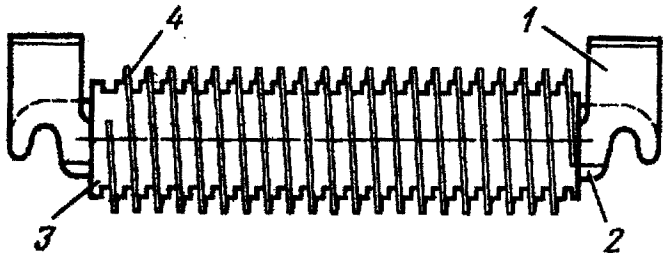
Внешний вид элемента резистора типа КФ
